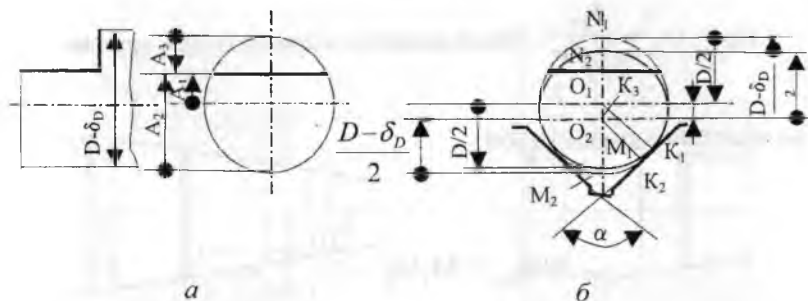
Схемы к определению погрешности установки цилиндрической заготовки на призме при различных схемах простановки операционного размера
